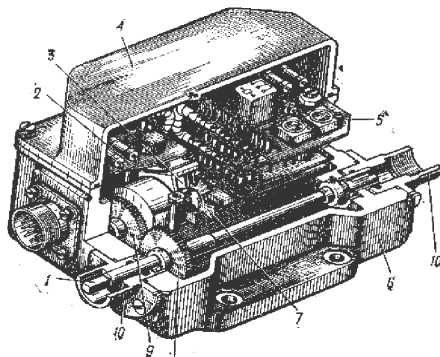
Механічний датчик швидкості. 1 - вал введення шляху; 2 і 5 - блоки електроелементів; 3 - індукційна котушка; 4 - кришка; 6 - корпус; 7 - діафрагма; 8 і 9 - шестерні; 10 - сполучні втулки.
